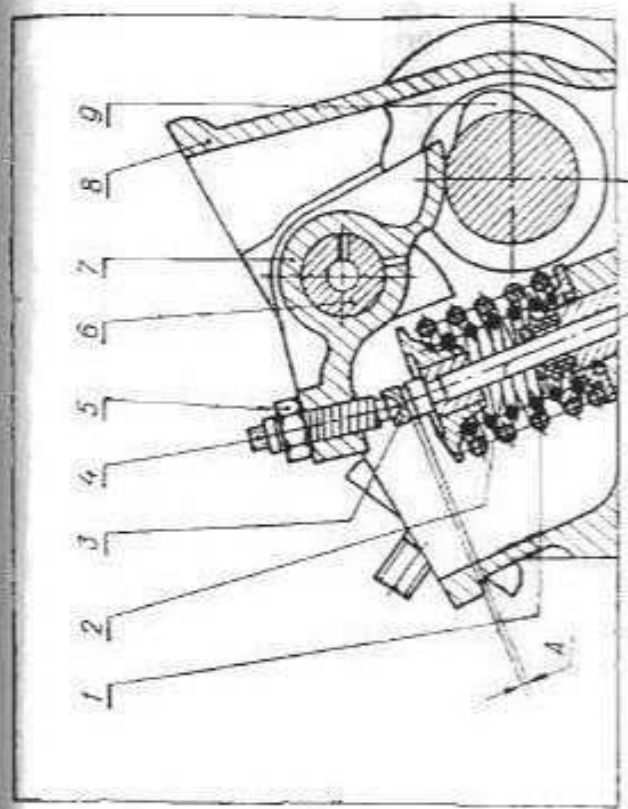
Регулировка зазоров в механизме привода клапанов:
